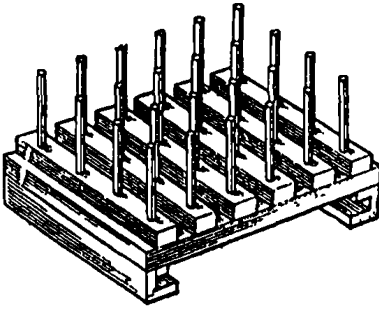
Тара для готовых деталей — подставка со свечами для шестерен
